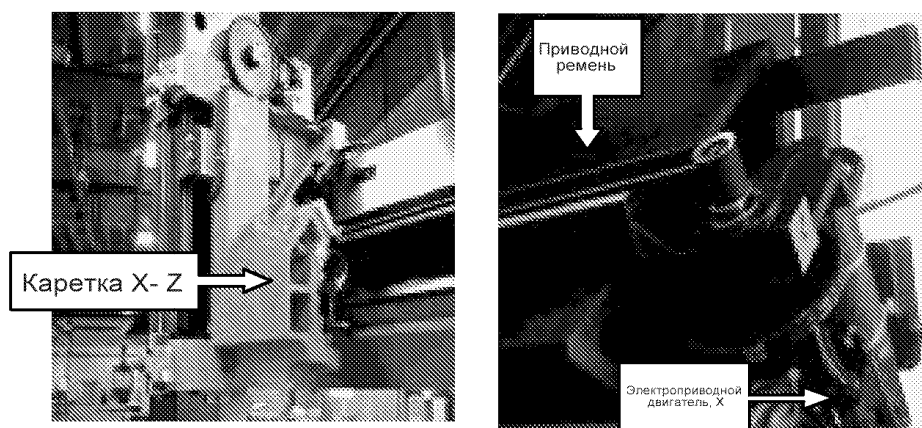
Каретка X-Z, Приводной ремень и электродвигатель
